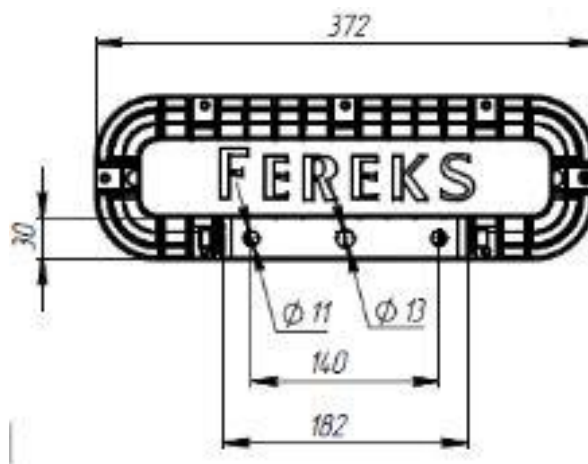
Габаритный вид подсветки FWL 14-28-W50-C120
